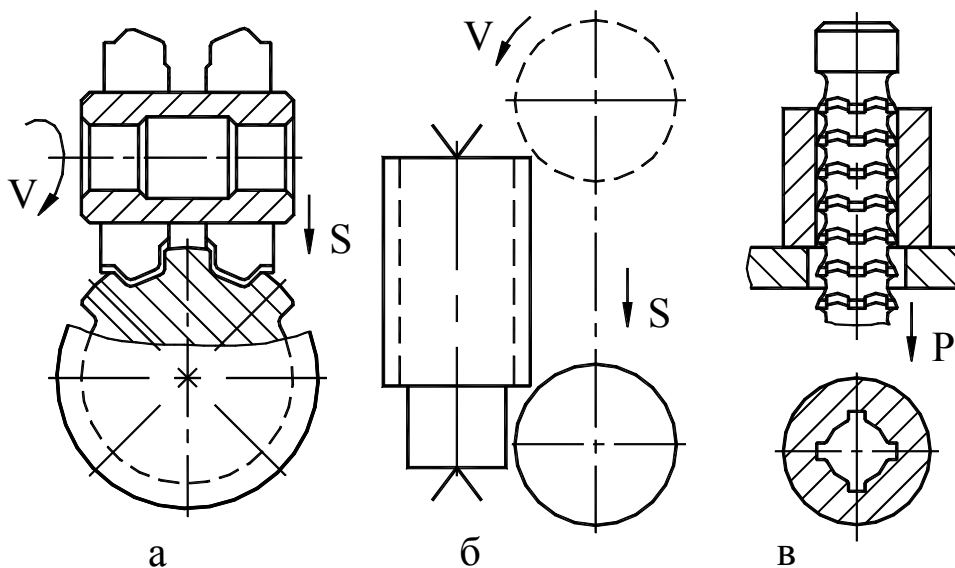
Схемы обработки шлицев: а – фрезерованием дисковой фасонной фрезой; б – фрезерованием червячной фрезой; в - протягиванием
